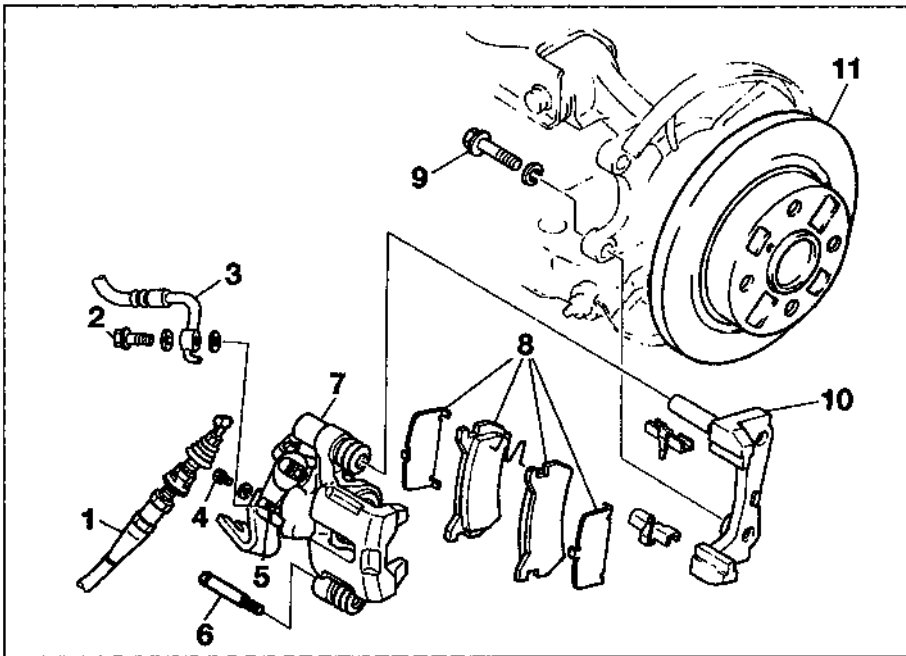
Детали суппорта дискового тормоза заднего колеса
